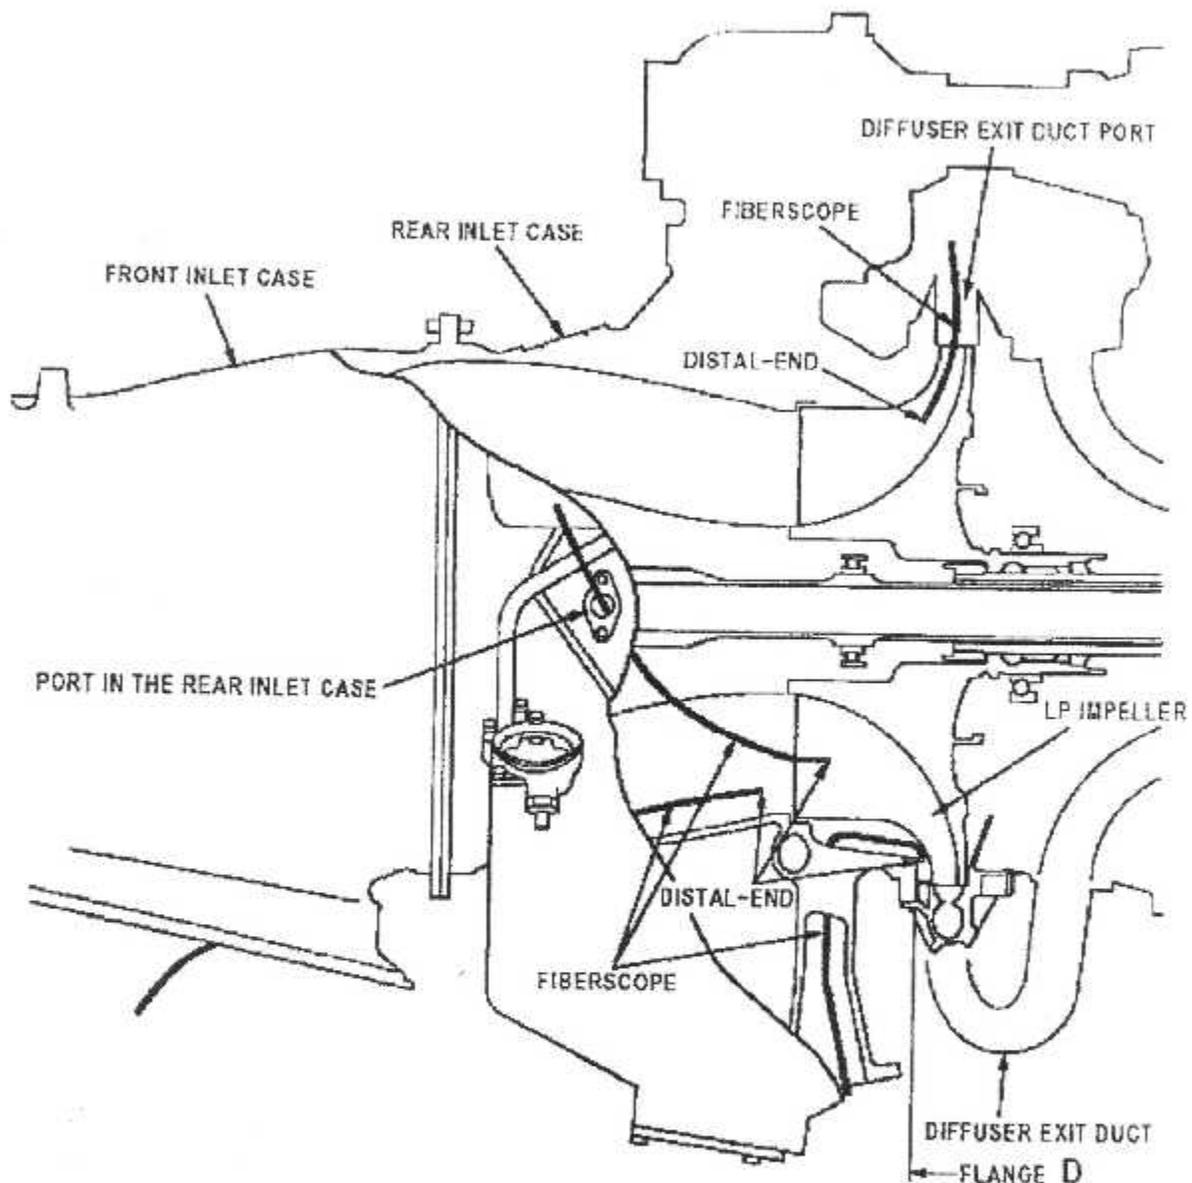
Inspection boroscopique du compresseur BP.
